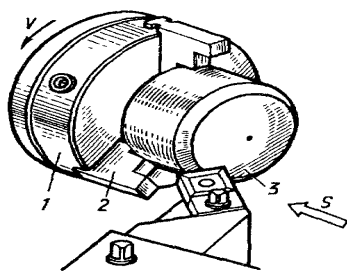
Закріплення заготовки у перевернутих кулачках патрона:
